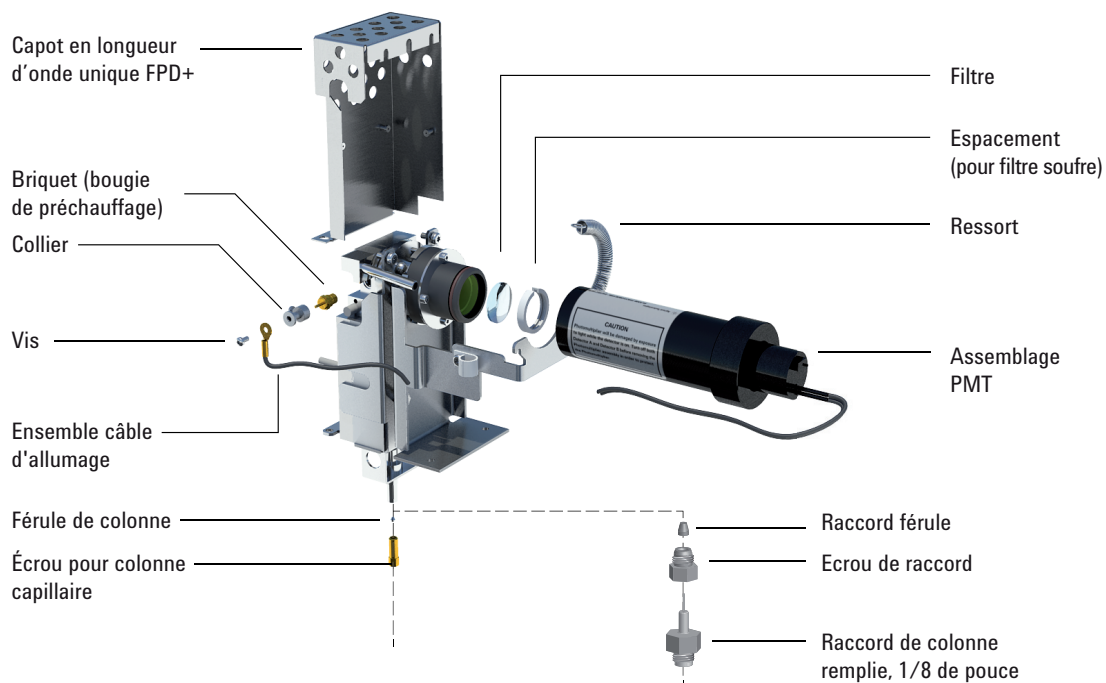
Vue éclatée des pièces du détecteur photométrique de flamme Plus (DIF+) longueur d'onde simple
